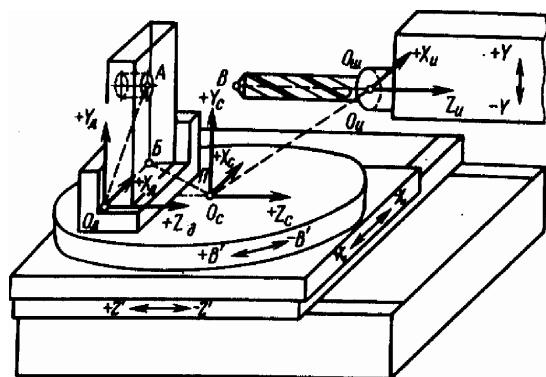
Схема связи систем координат детали и инструмента сверлильно-фрезерно-расточного станка с ЧПУ
